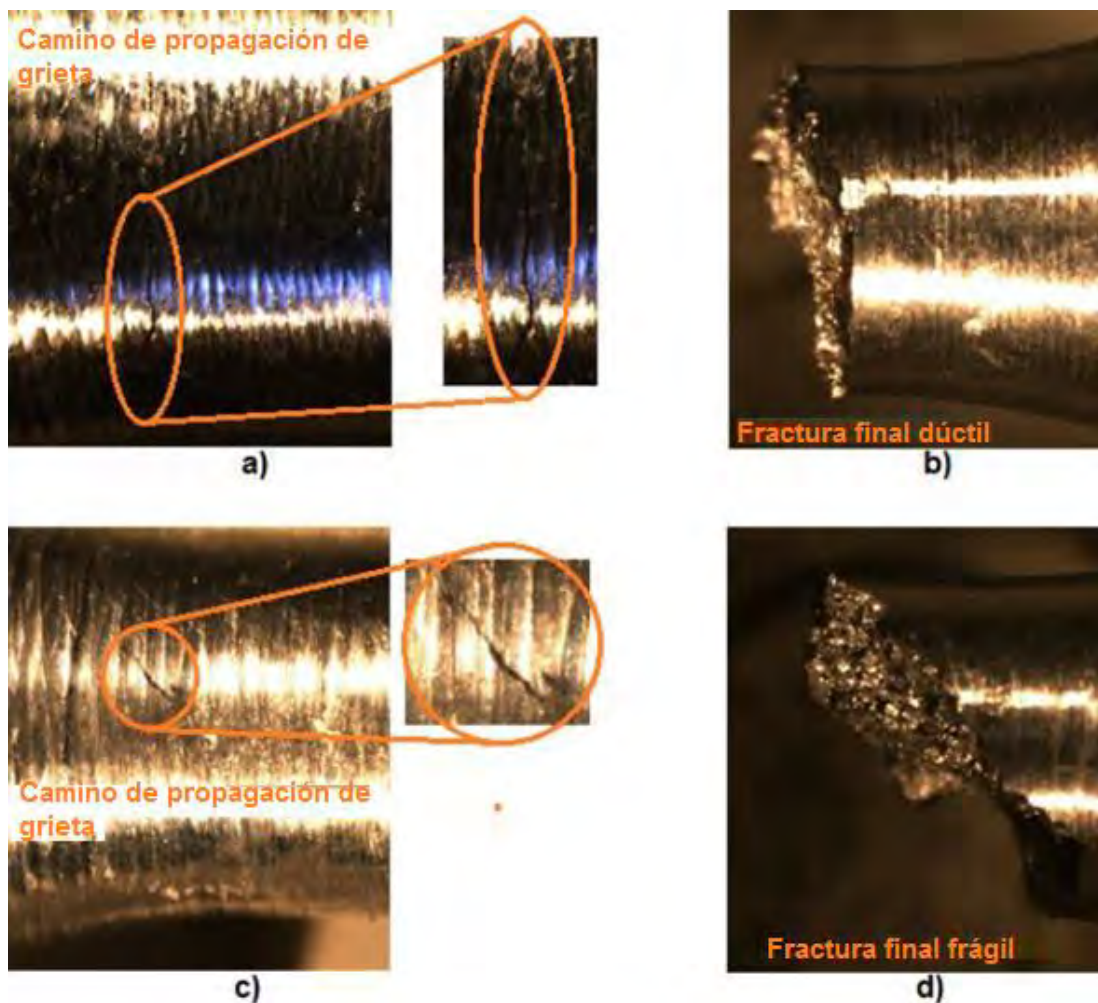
Caminos de grieta para ensayos de fatiga por torsión: grieta dúctil, perpendicular al eje principal del espécimen a) b), grieta frágil a través de un ángulo cercano a 45° .
